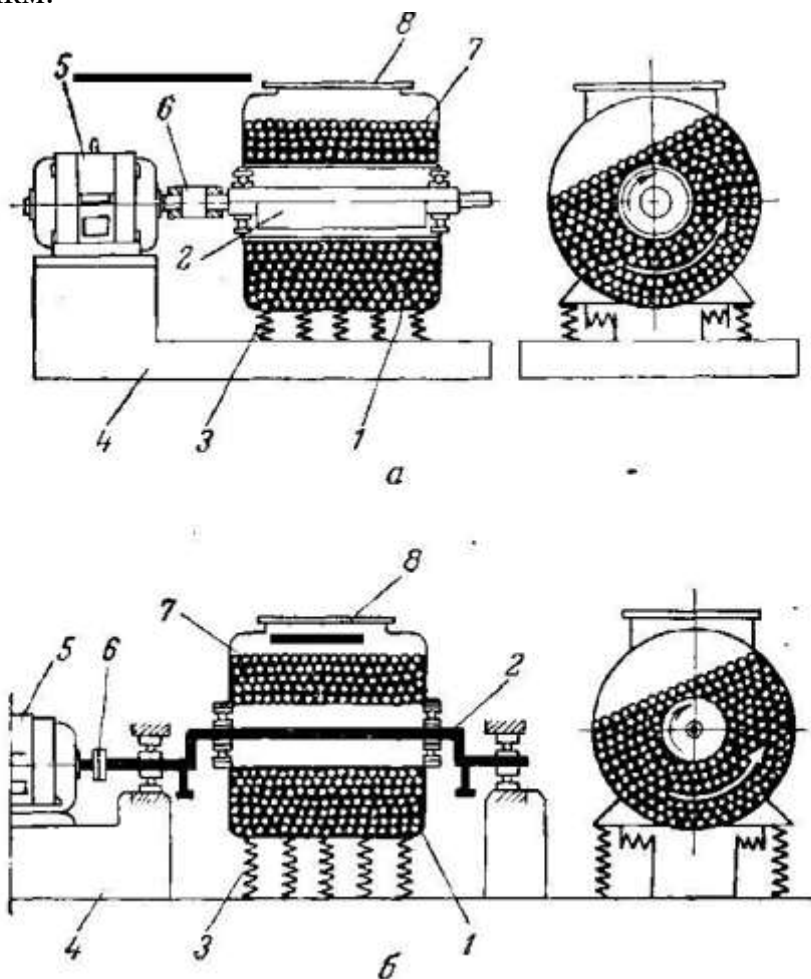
Схема вибрационной мельницы с внутренним вибратором: а – инерционным; б - вибрационным; 1 – корпус; 2 - вибратор; 3 - опоры; 4 - рама; 5 – электродвигатель; 6 - муфта; 7 - мелющие тела (шары); 8 – люк.
